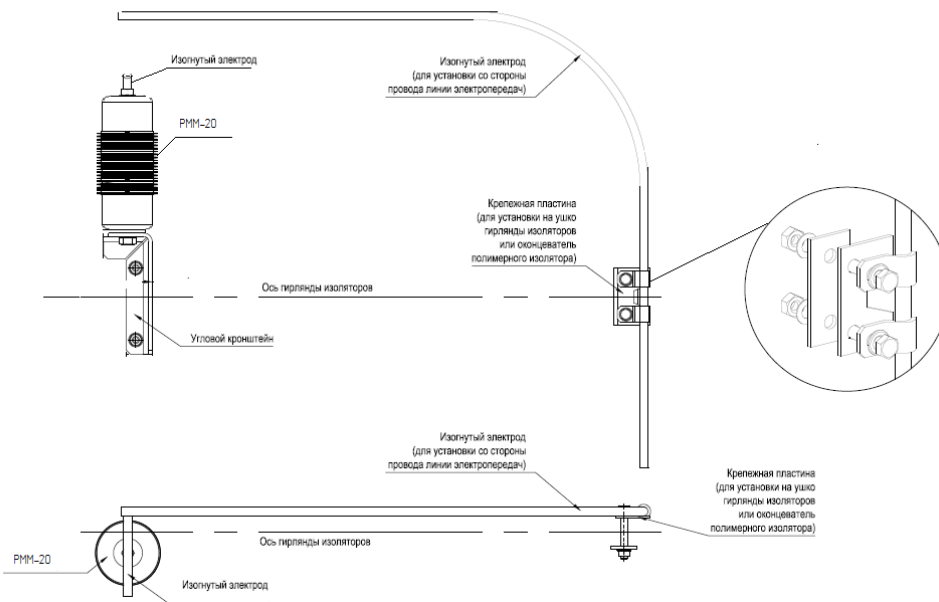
Комплект деталей для установки устройства RMM-20 на промежуточную опору с натяжными изоляторами.
